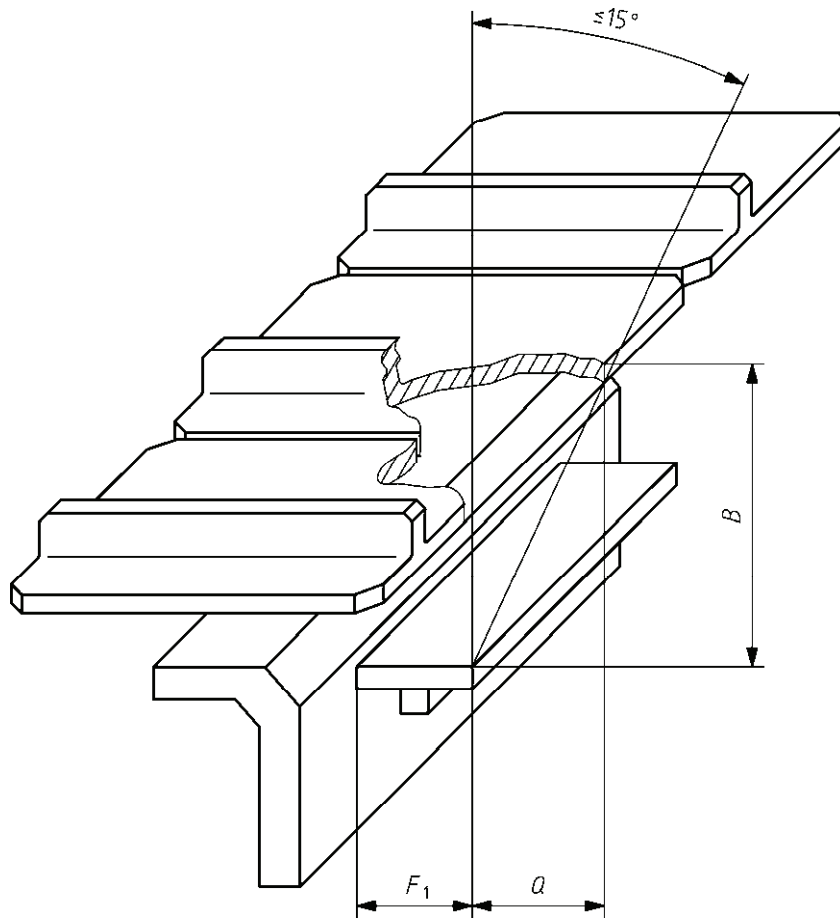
Mindest-Freiraum für die unteren Gliedmaßen im Zugangsbereich zum Maschinenführerplatz bei Maschinen mit Knicklenkung
